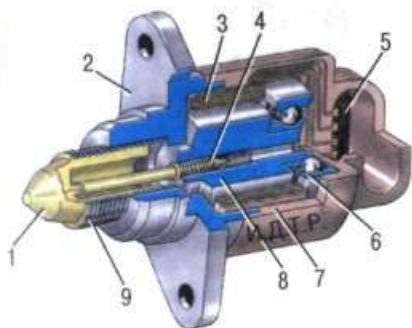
Регулятор холостого хода: 1 – клапан; 2 – корпус регулятора; 3 – обмотка статора; 4 – ходовой винт; 5 – штекерный вывод обмотки статора; 6 – шариковый подшипник; 7 – корпус обмотки статора; 8 – ротор; 9 – пружина
